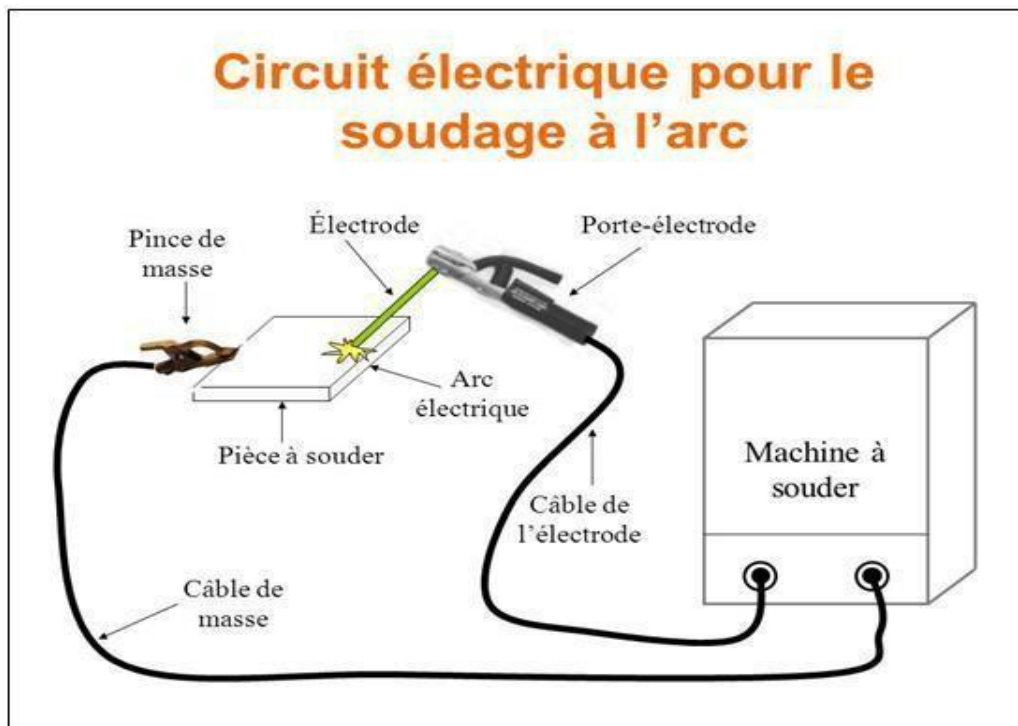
Installation du circuit de soudage SMAW
